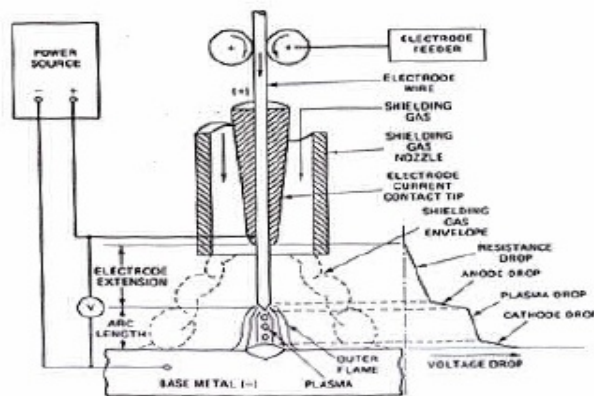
Mesin Las (*Gas Metal Arc Welding*).
